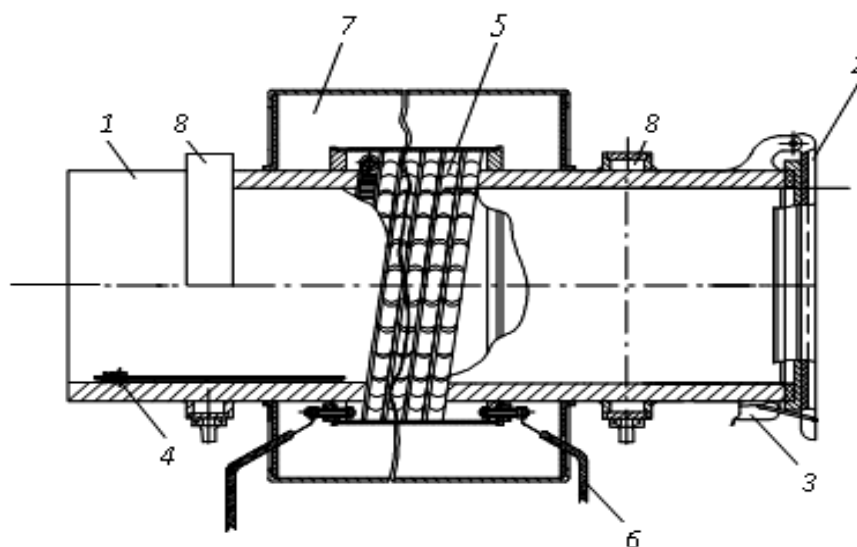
Цилиндрическая однокамерная печь сопротивления для воздушно-термического оксидирования: 1 – камера; 2 – крышка; 3 – защелка; 4 – термопара; 5 – нагревательный элемент; 6 – электрические выводы; 7 – кожух; 8 – система охлаждения
